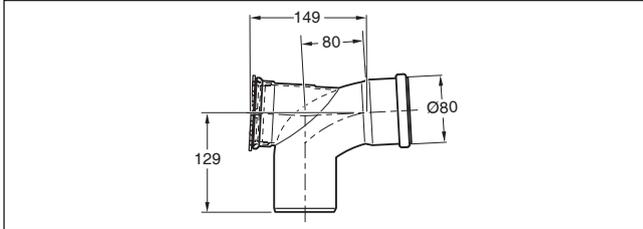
Bogen mit Prüföffnung lang (Maße in mm)
